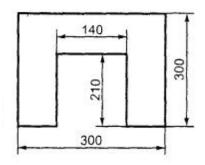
Скоба для фиксации деталей при сборке
